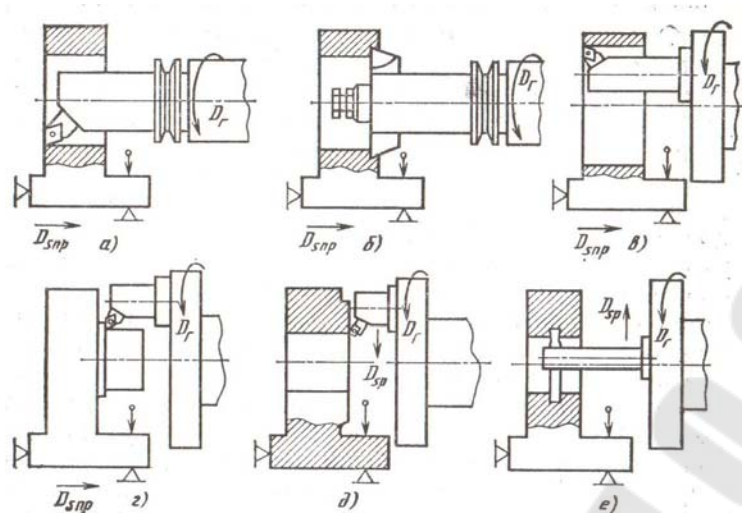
Схемы обработки поверхностей на расточных станках: а – растачивание отверстий; б – подрезание торцов; в – растачивание отверстий очень большого диаметра; г - обтачивание цилиндрических наружных поверхностей; д – обработка наружных торцевых поверхностей; е – изготовление внутренних канавок
